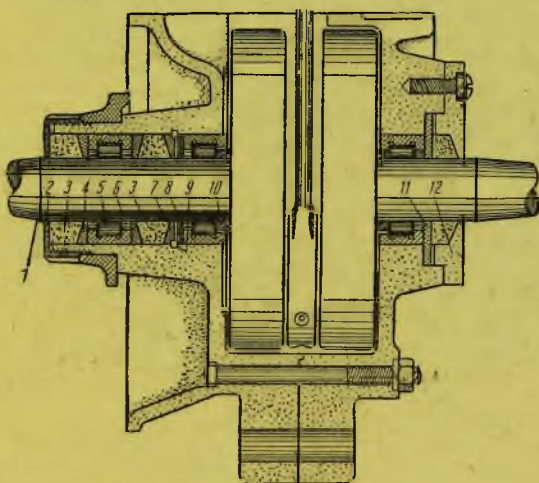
Сальники коренных подшипников ИЖ-7 и Л-300
